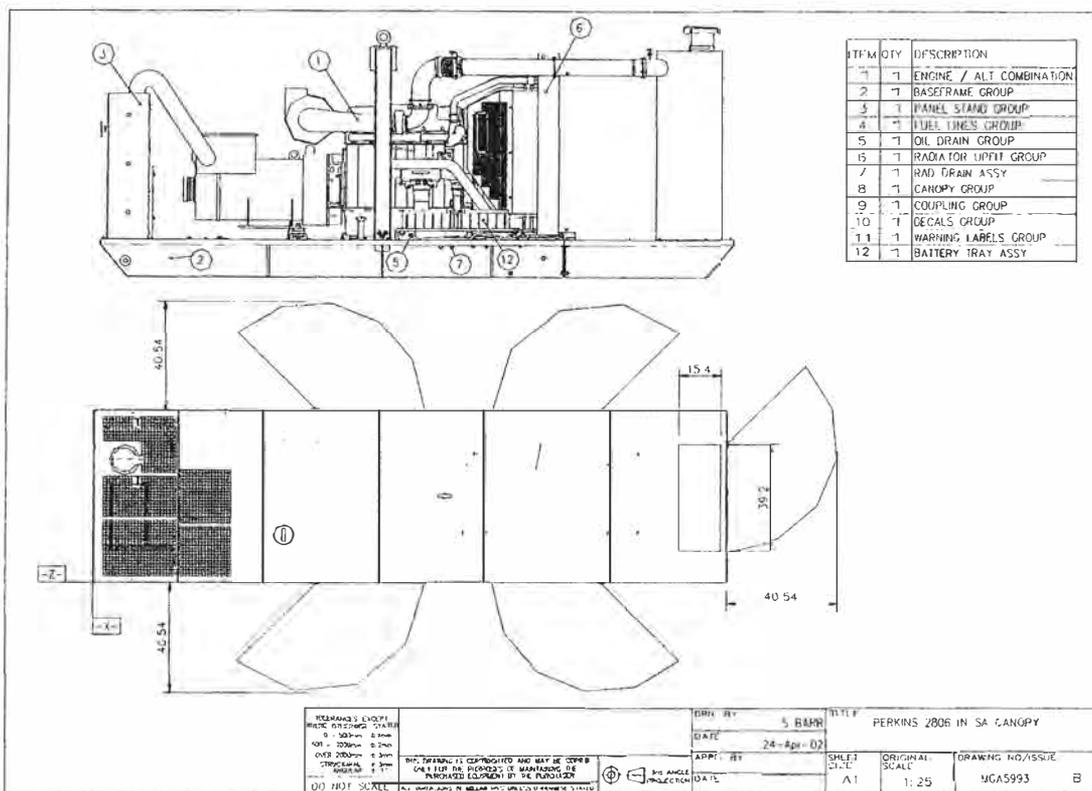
, Vista lateral y de planta de grupo electrógeno (Perkins 2806).
